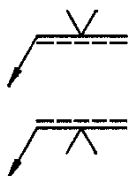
Soldadura en el lado de la flecha
